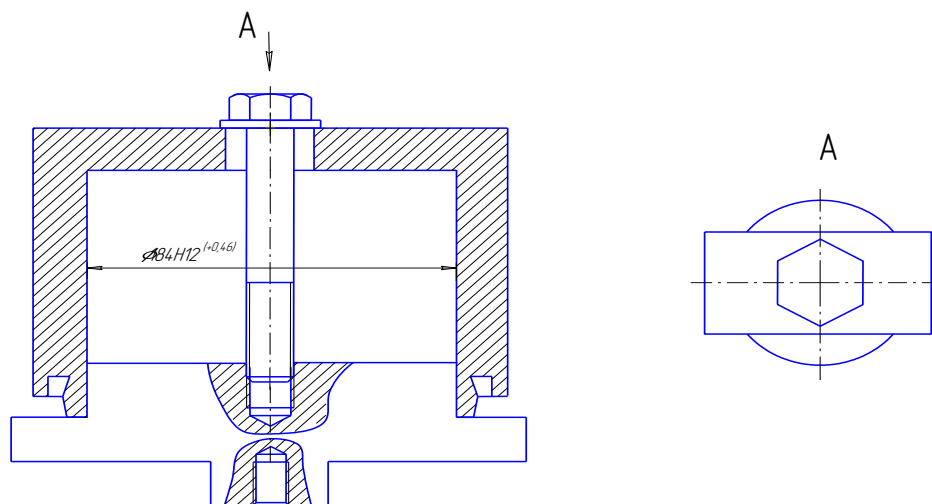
Пристосування для базування і закріплення заготовки для координатно-розточний операції
